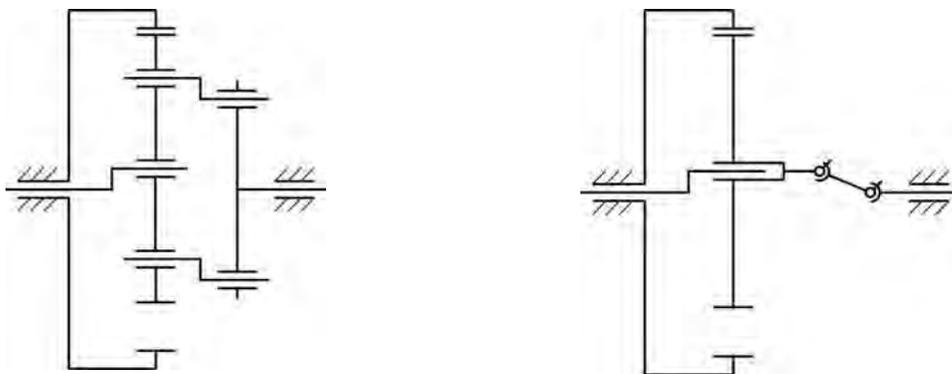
Кинематические схемы эксцентриковой передачи типа К-Н-V
